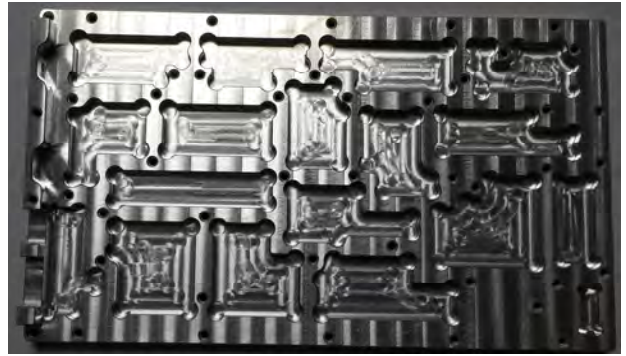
알루미늄 차폐 격자를 적용한 PCB
